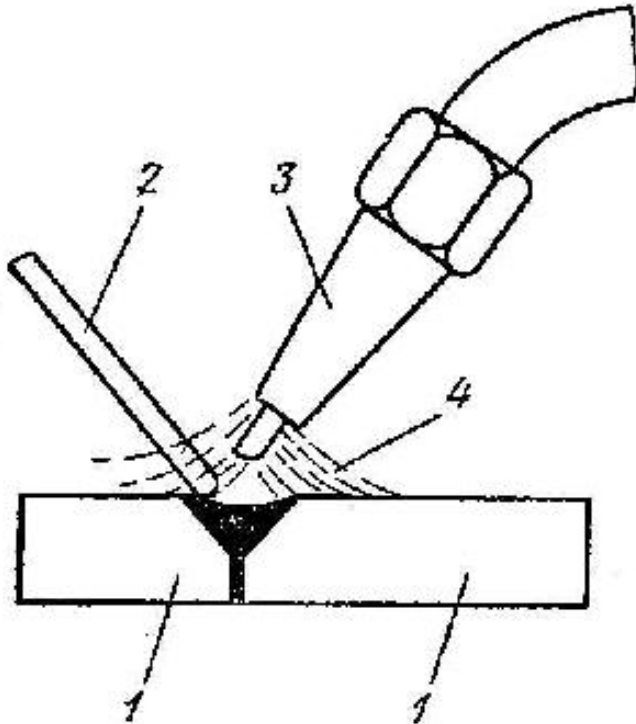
Схема газовой сварки: 1 – свариваемые заготовки, 2 – присадочный пруток, 3 – горелка, 4 – пламя
